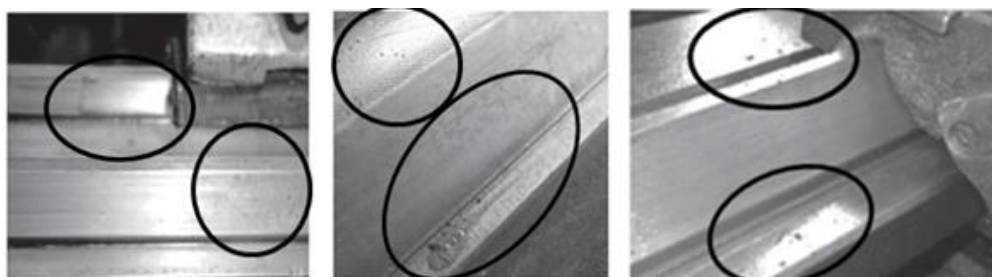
Внешний вид направляющих металлорежущих станков с износом и повреждениями
